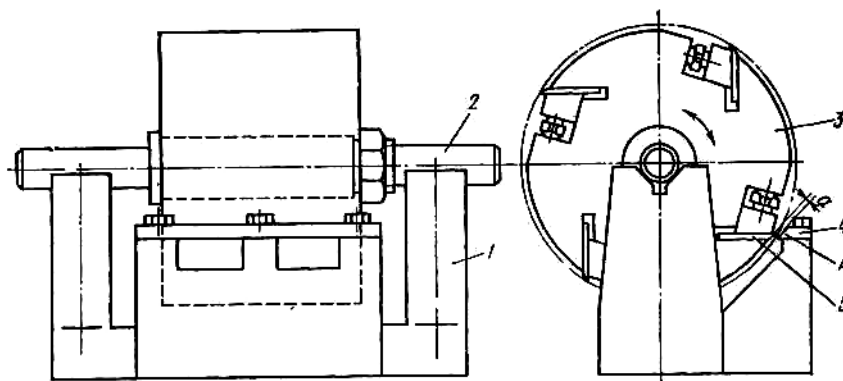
Приспособление для установки ножей в ножевую головку четырехстороннего продольно-фрезерного станка: *1* — основание, *2* — оправка, *3* — ножевая головка, *4* — планка, *5* — нож
